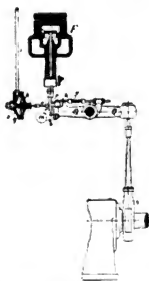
Deutzer Brennstoffpumpe mit Membransteuerung.
